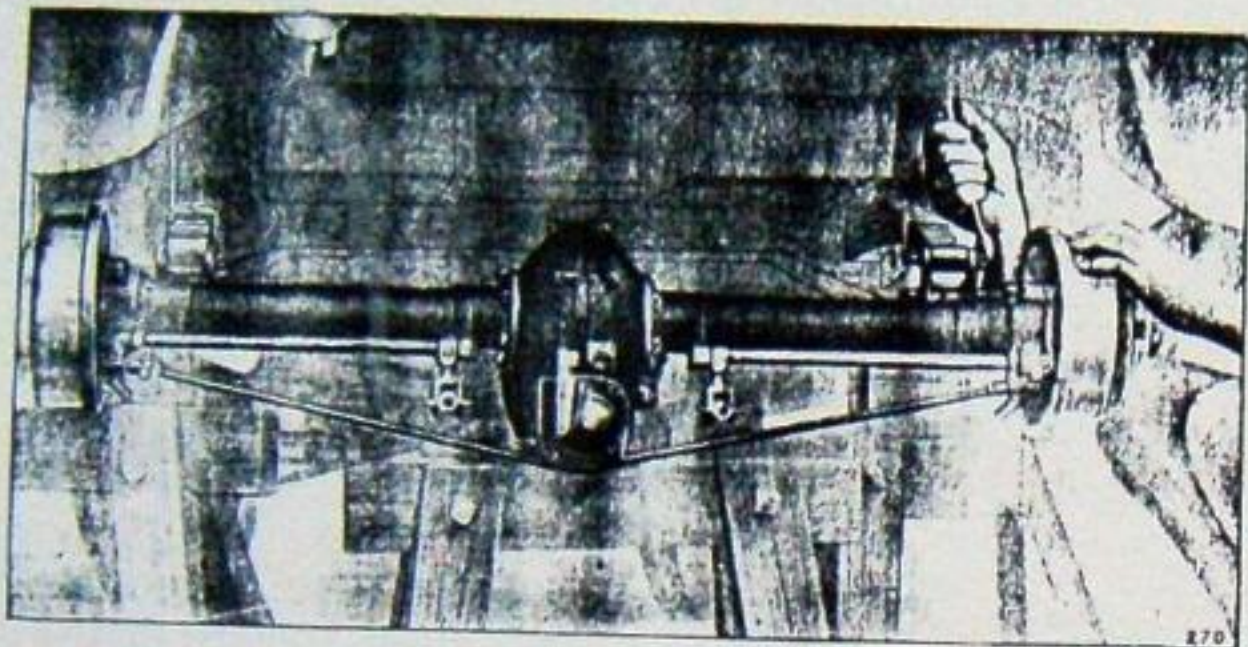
Desserrage de l'écrou d'un axe de ressort arrière.
